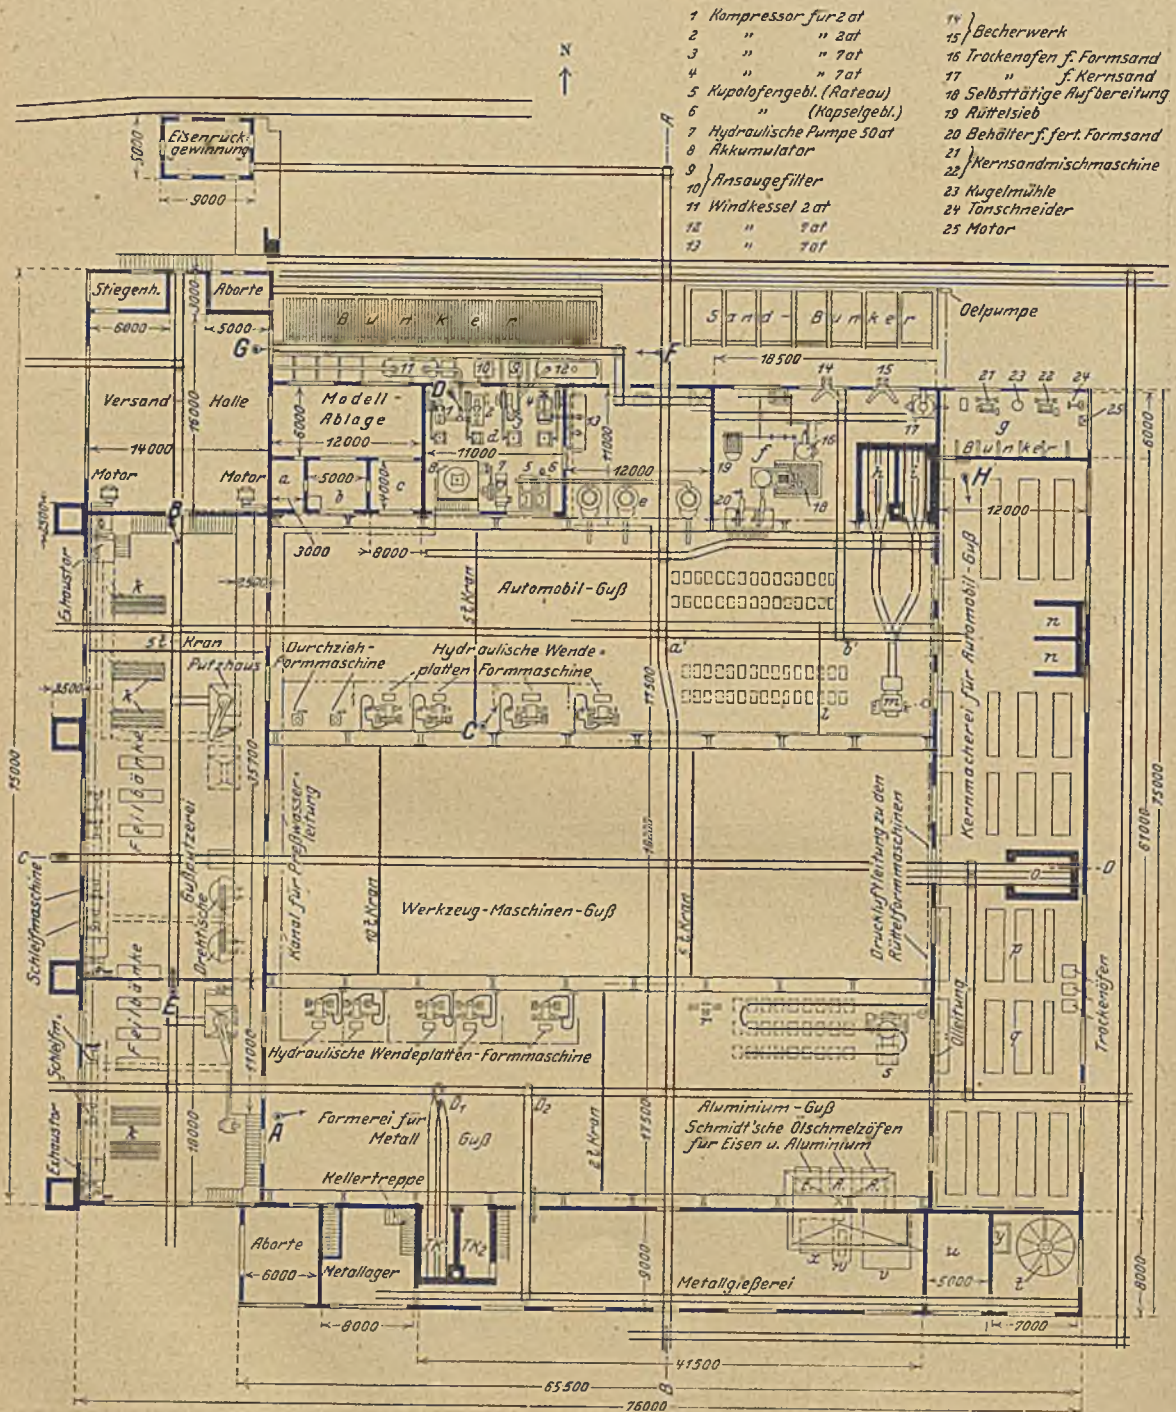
Grundrisse der gesamten Gießereianlage.
